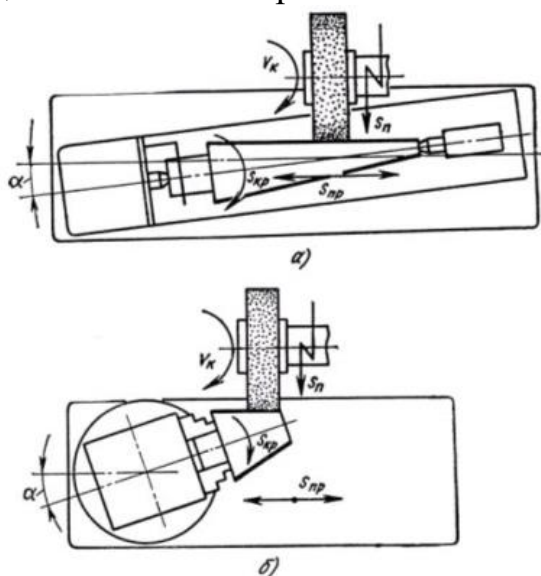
Схемы шлифования конических поверхностей заготовок
